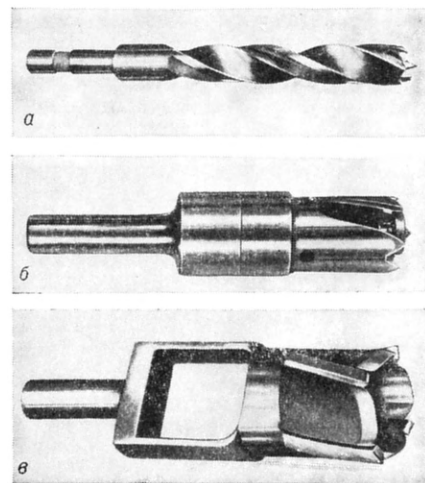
Сверла для обработки древесины и древесных материалов: а — спиральное с направляющим центром и подрезателем; б — цилиндрическое полое с выталкивателем для высверливания пробки; в — для кольцевого сверления.
